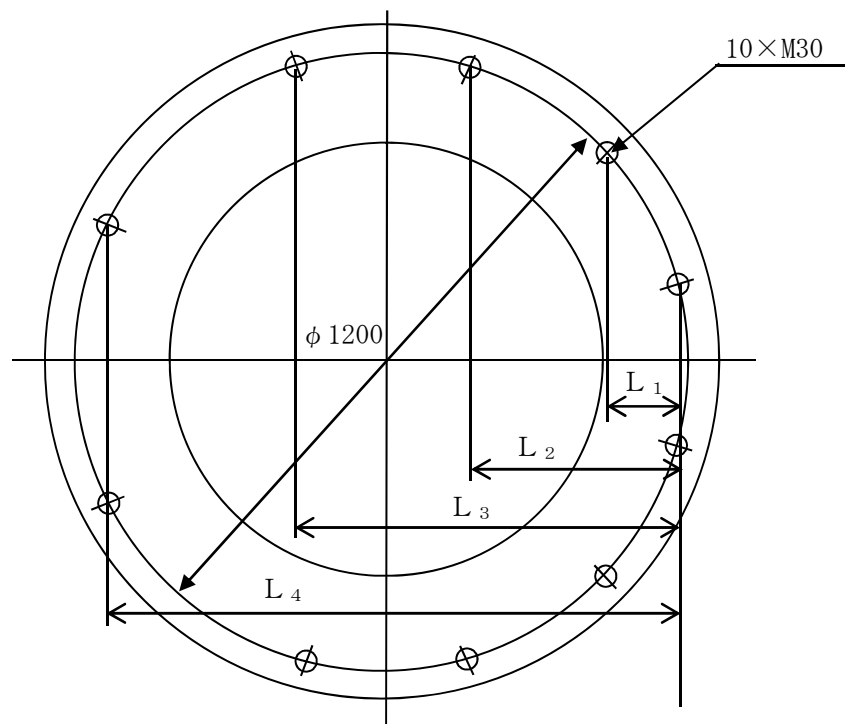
原動機台取付ボルトの各ボルト間寸法の配置図
